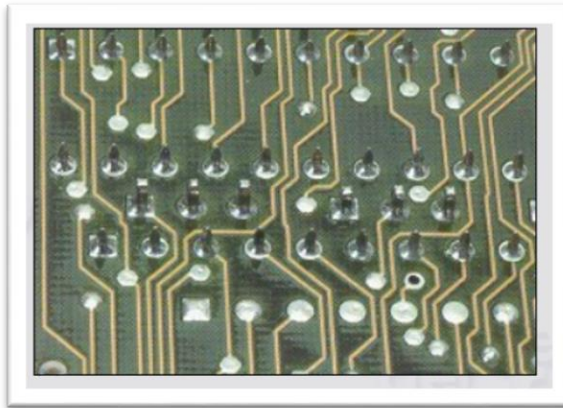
(Placa PCB Soldada con estaño)
